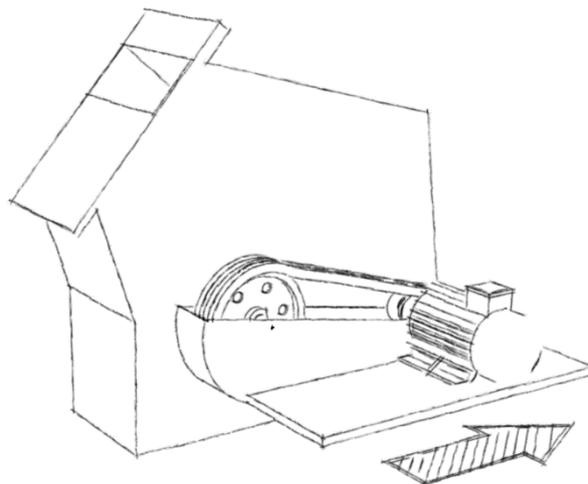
14 Sketsa Pelepasan *Cassing Motor Penggerak
